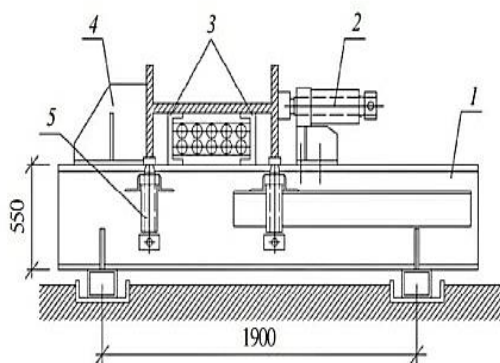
Кондуктор з гвинтовими притискачами для складання зварних двотаврів: 1 - рама; 2 - гвинтовий притискач; 3 - підставка; 4 - нерухомий упор; 5 - гвинтові упори
